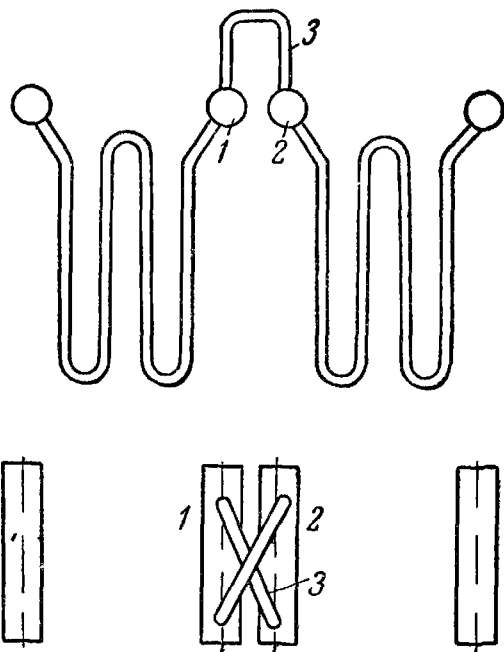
Компоновка пароперегревателя из двух пакетов.
